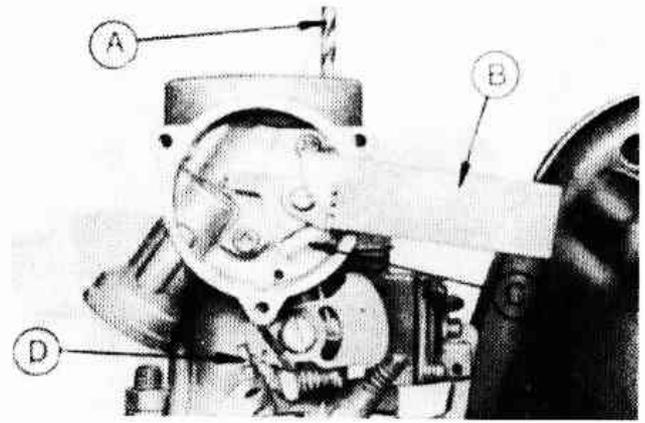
Регулировка хода — сверло (A), приспособление для предварительной нагрузки (B), регулировочный рычаг (C), дроссельная заслонка с поднятым кулачком (D) (Разд.24)
